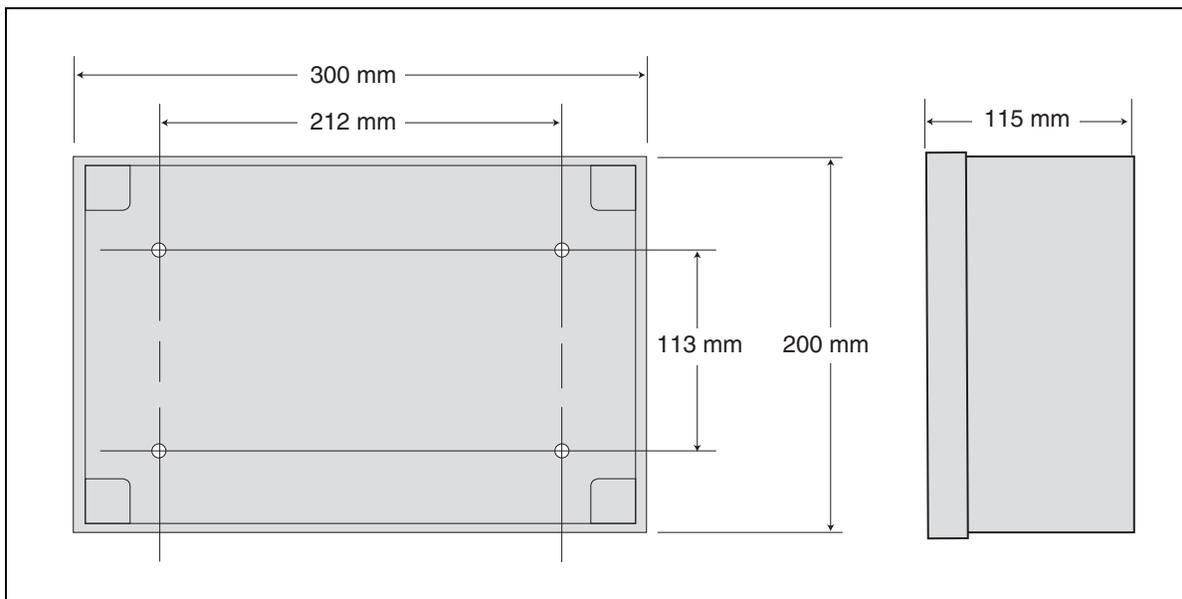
Caixa de Terminais TLS – Dimensões Gerais e de Fixação
